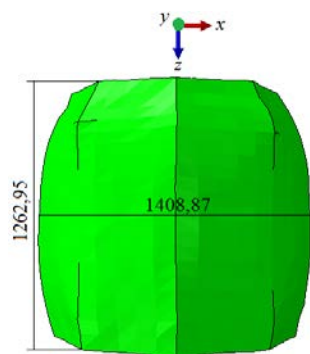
Формоизменение боковой поверхности стальной заготовки после прессования
